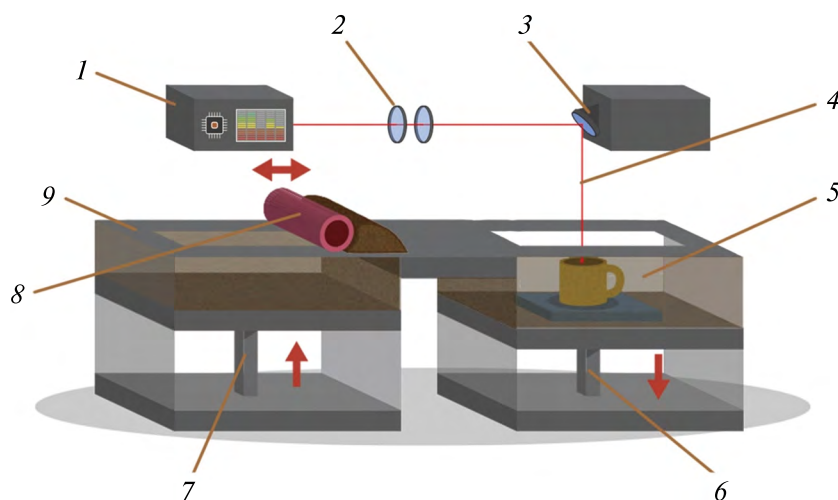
Схема работы 3D-печати расплавлением порошкового материала:
